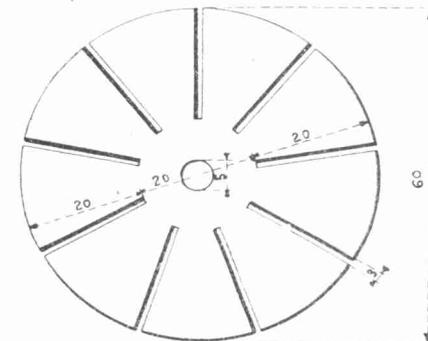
Dimensions des gallettes pour bobinages en fond de panier.
